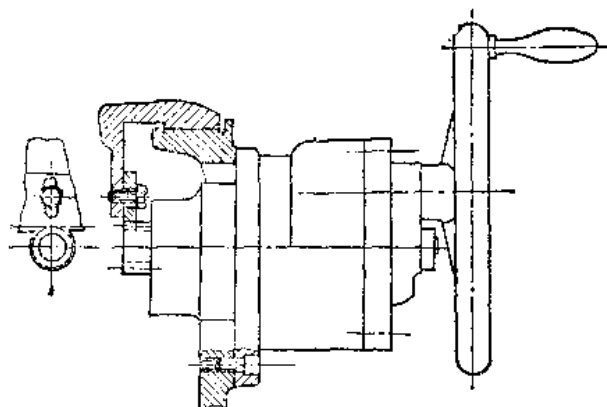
利用长孔来调节齿条与齿轮的啮合位置
